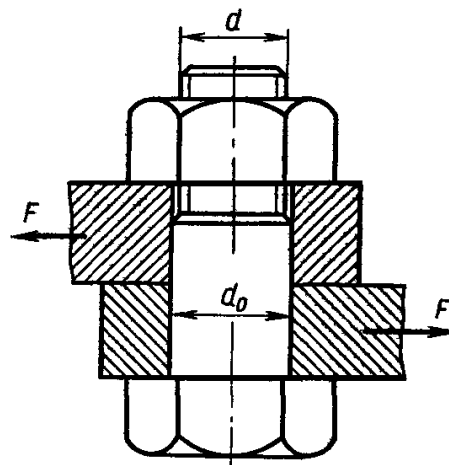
Болт, установленный в отверстие из-под развертки без зазора, нагруженный поперечной силой
